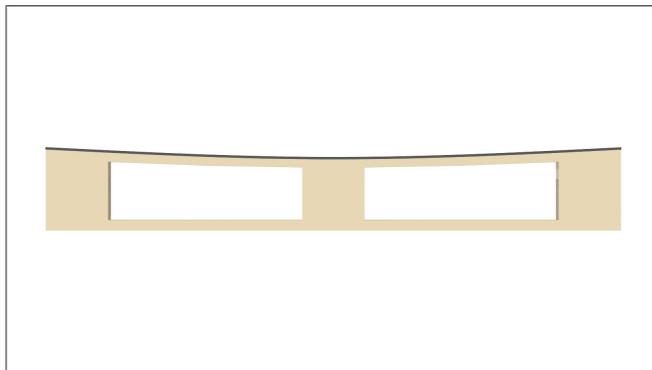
Paleta abaulado, baixado para baixo (superfície côncava)
